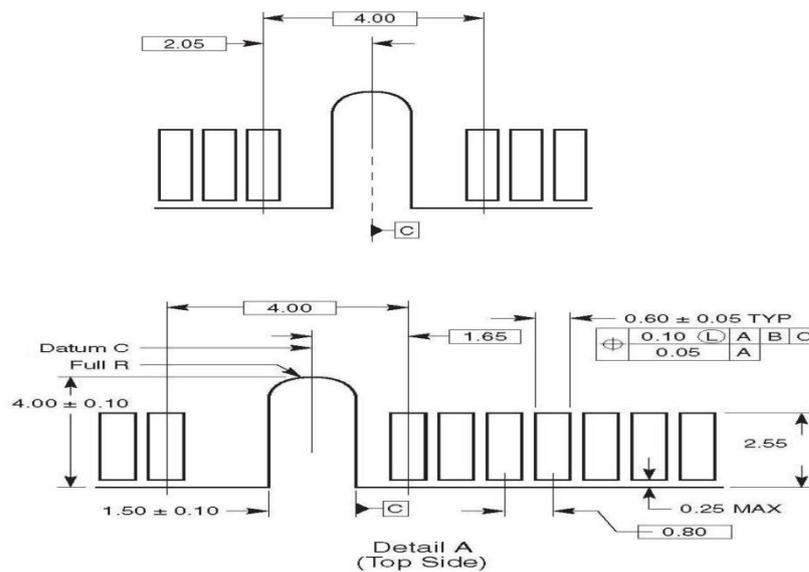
金手指 TOP 和 BOTTOM AB 处细节尺寸
